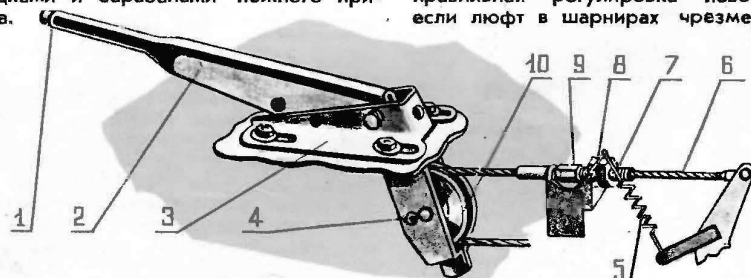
Ручной тормоз: 1 — кнопка рычага; 2 — рычаг тормоза; 3 — кронштейн; 4 — ось ролика; 5 — оттяжная пружина; 6 — трос; 7, 8 — регулировочные гайки; 9 — наконечник оболочки троса; 10 — ролик.
